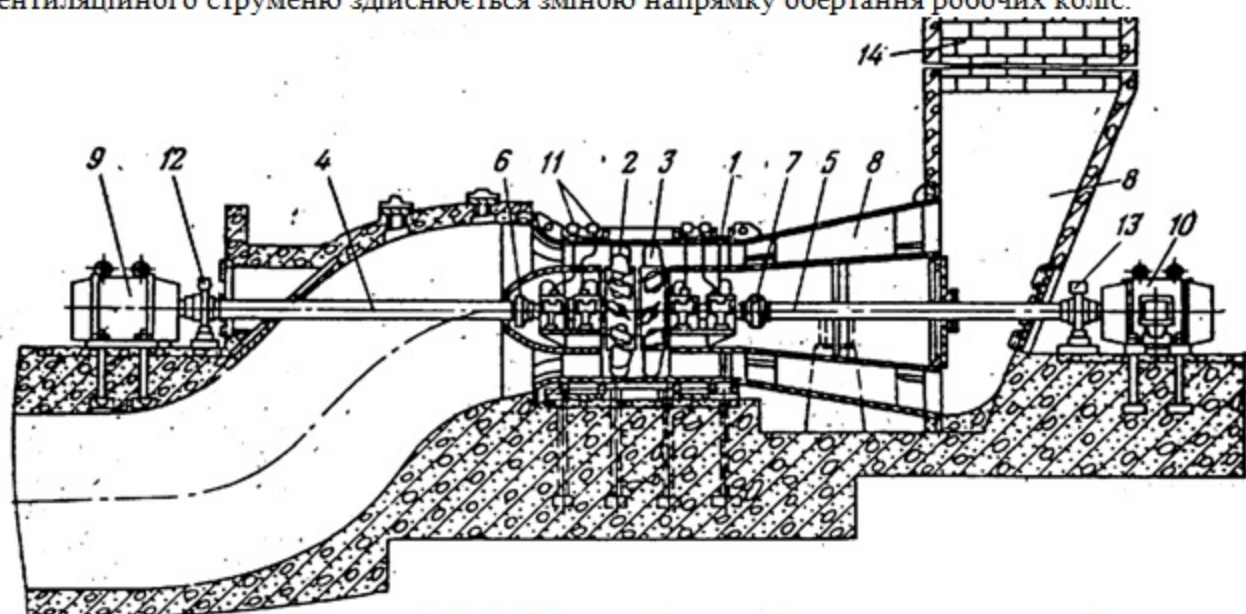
Вентилятор ВОД-16 із зустрічним обертанням робочих коліс
